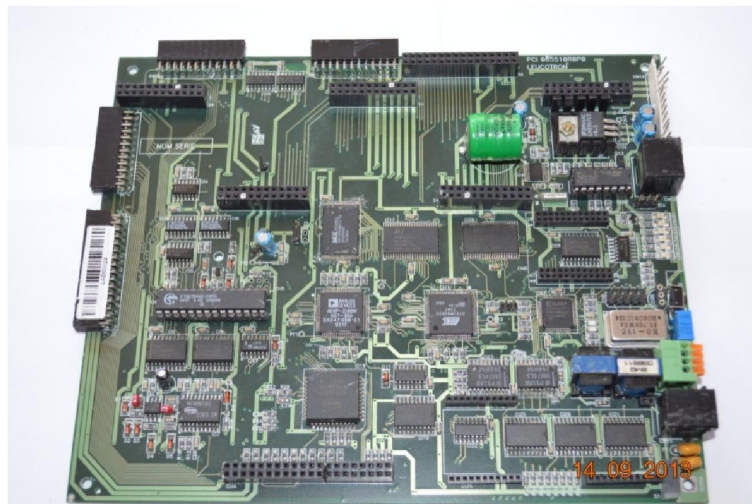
Placa de circuito impresso com os componentes eletrônicos montados
